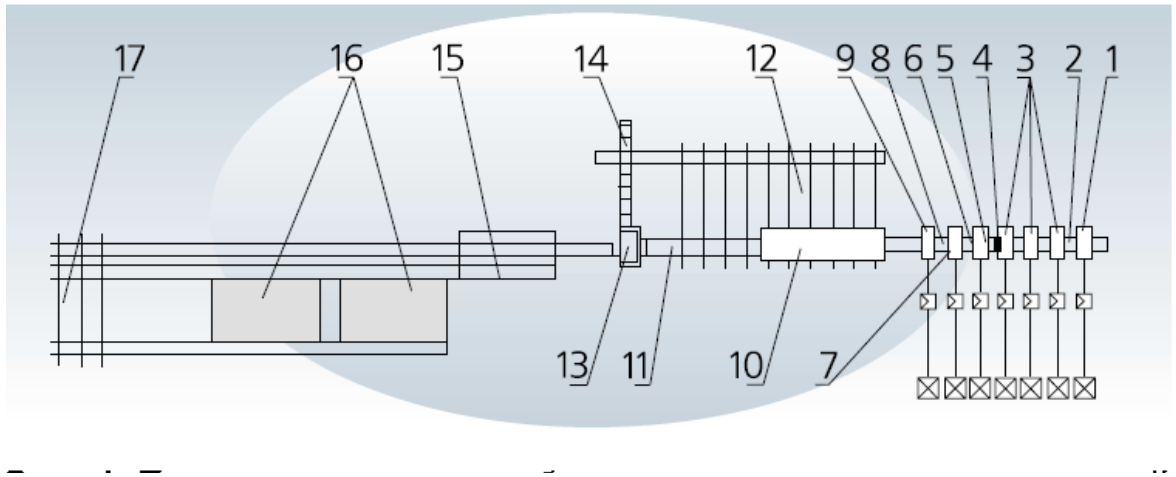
Схема багатострумкової прокатки квадрата 80: 1-8 -
